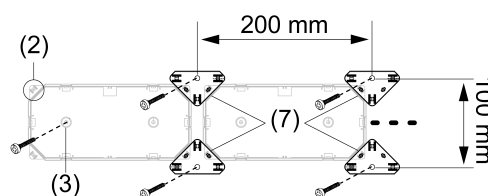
Montage mit Verbindern: LED-Lampe PR100
